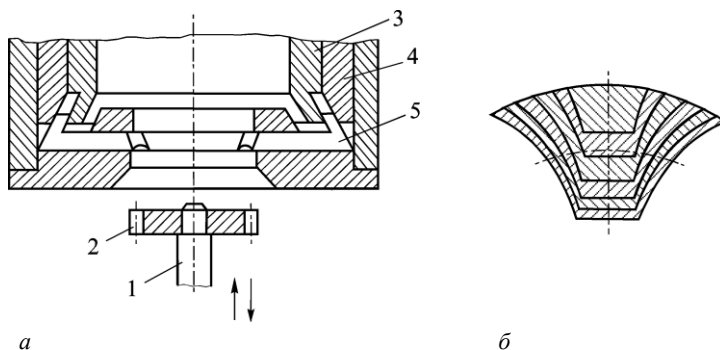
Нарезание зубчатых колес зубодолбежной головкой:
